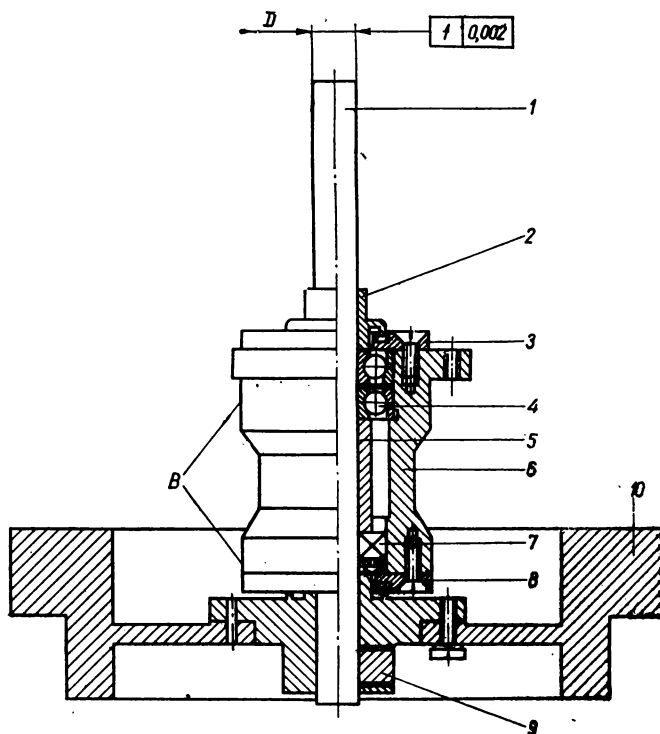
Конструкция сверхпрецизионного узла ведущего вала исполнения II.
